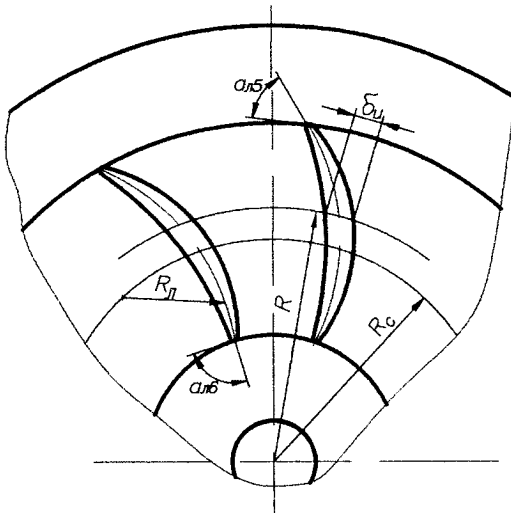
Схема лопаткової решітки із профільованими лопатками
